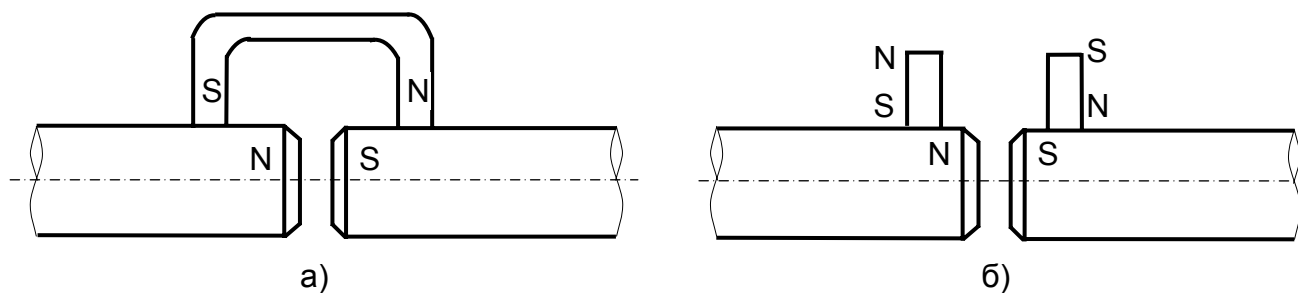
Схема размагничивания сварных соединений постоянными магнитами
